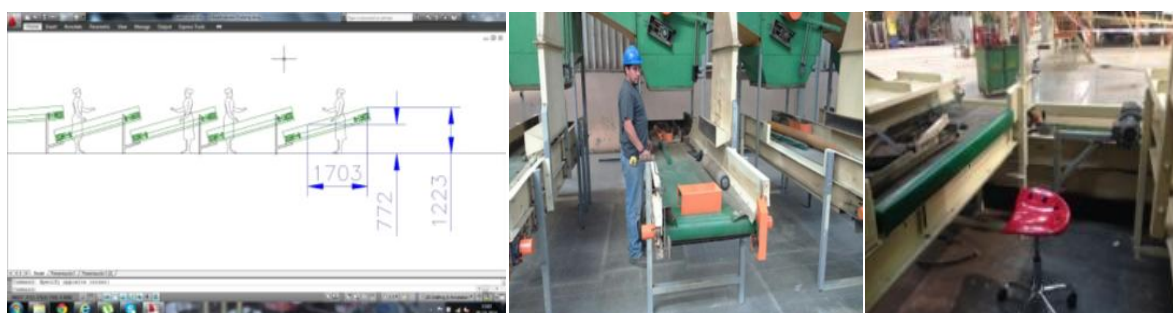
Anteproyecto y avances presentados por el equipo de trabajo planta BAT San Fernando.
